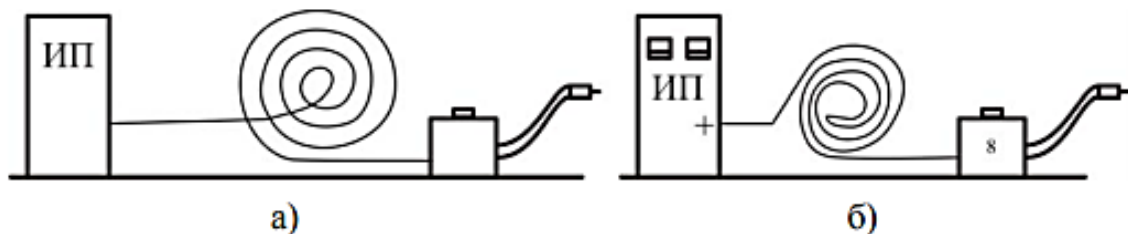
Схемы размещения сварочных кабелей, создающих индуктивность сварочной цепи: а) повышенную; б) пониженную
